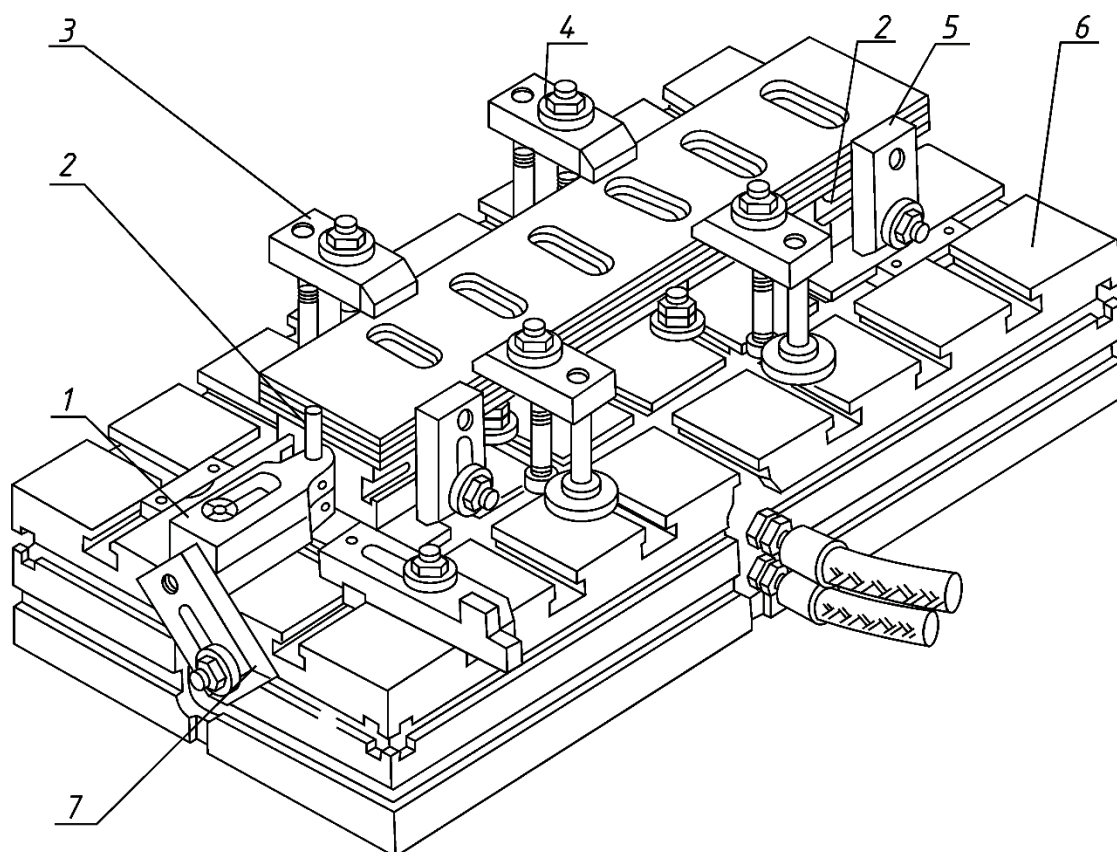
АСП для обработки пазов сепаратора: 1 – опора с базовыми пальцами; 2 – базовые установочные пальцы; 3 – прихват; 4 – гайка крепления; 5 – базовые планки; 6 – базовая плита; 7 – планки
